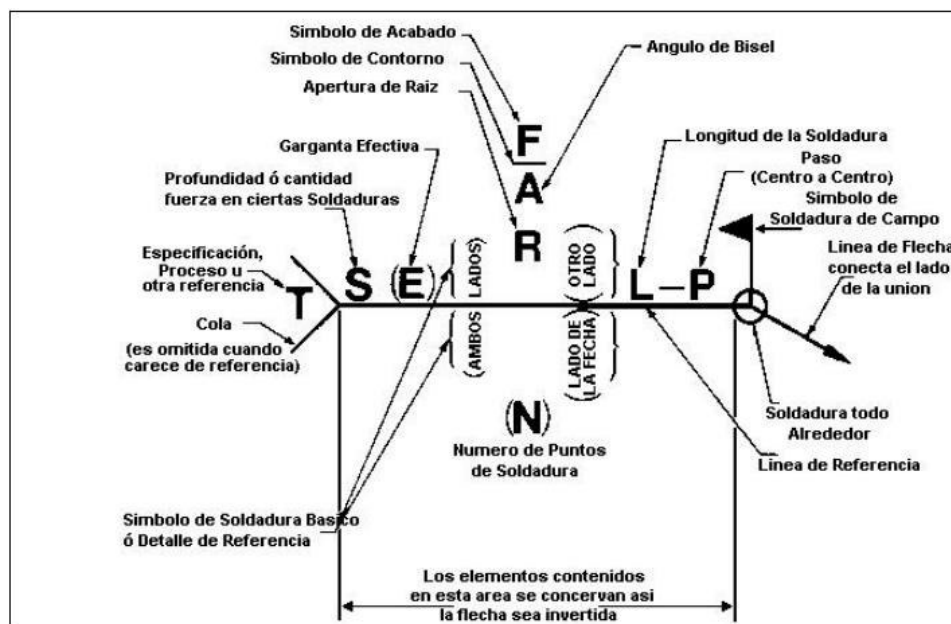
Se puede ver el patrón de la AWS para símbolos de soldadura [30].
